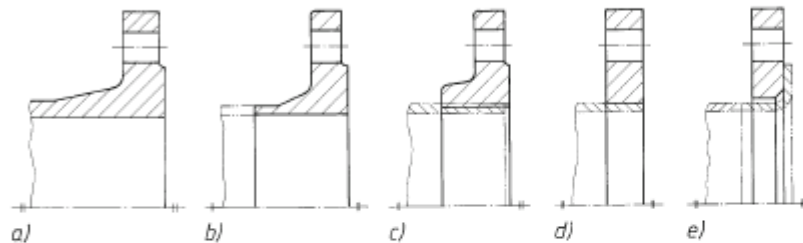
Genormte Flansche. a) Gusseisen- und Stahlgussflansch, b) Vorschweißflansch, c) Gewindeflansch mit Ansatz, d) glatter Flansch zum Lötten oder Schweißen, e) loser Flansch für Bördelrohr
